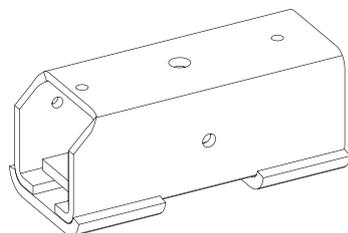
Support à souder (support : acier, nu ; petites pièces : acier, galvanisé)
